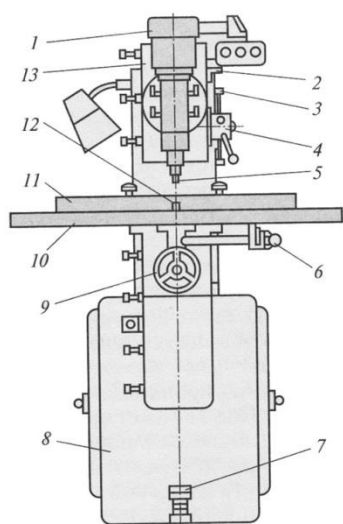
Одношпиндельный фрезерный станок с верхним расположением шпинделя: 1- электрошпиндель; 2- упор; 3- винт-ограничитель; 4- поворотная головка; 5 – фреза; 6- ручка; 7- педаль; 8- станина; 9- маховичок; 10- стол; 11- направляющая линейка; 12- палец; 13 – суппорт
